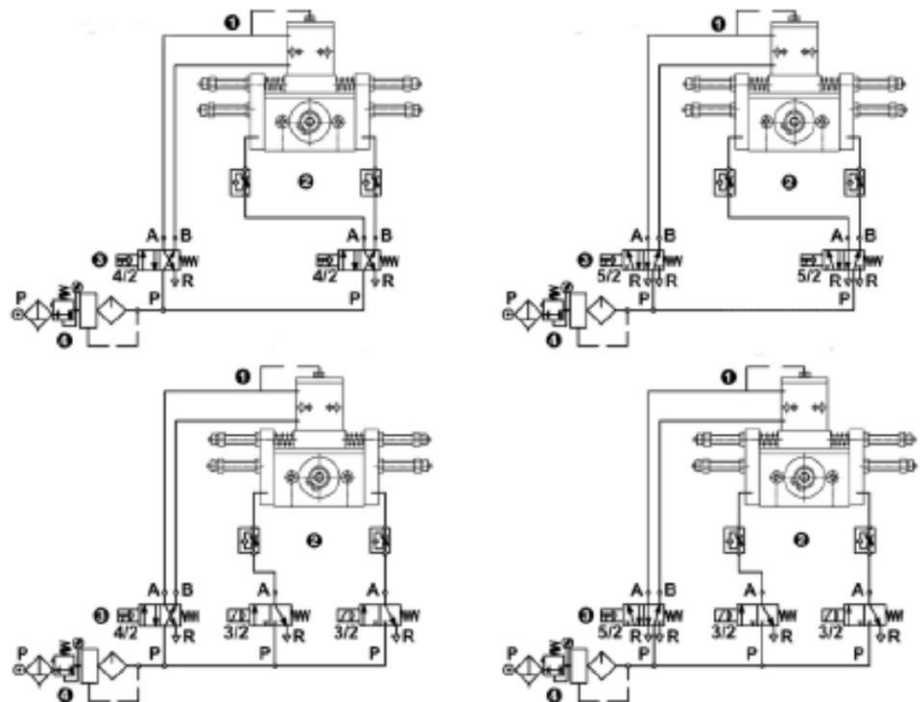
Pneumatik-Schaltplan Rotationsmodul RM 16
